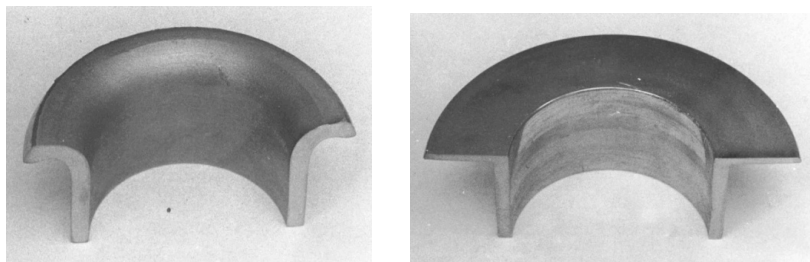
Заготовка із сталі 12Х18Н10Т, відбортована розкочуванням (на проміжному і заключному етапах)
